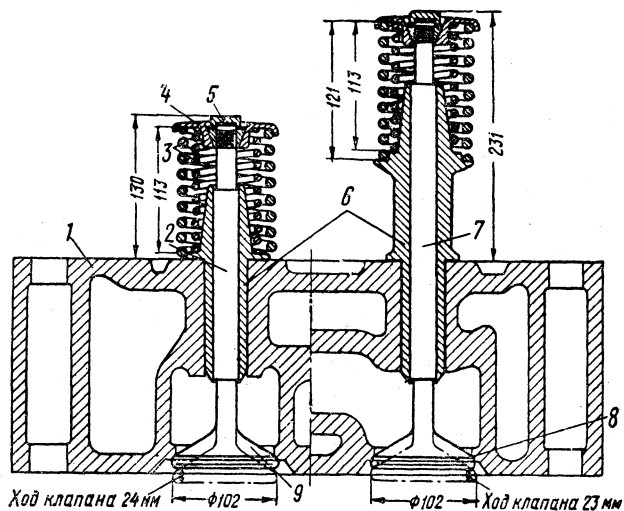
Расположение клапанов в цилиндровой крышке дизеля 2Д50:
